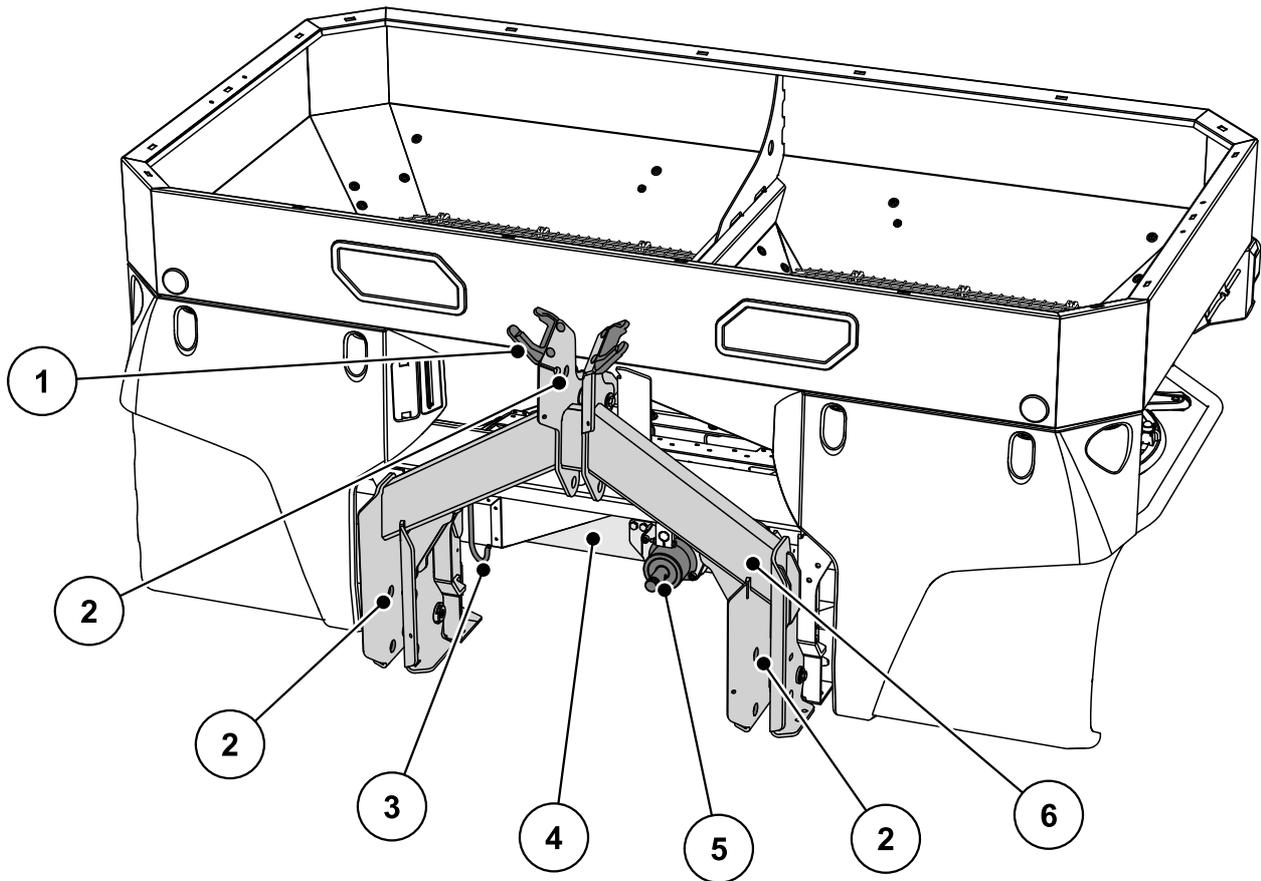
Aperçu des composants : Exemple AXIS 30.2, vue avant
